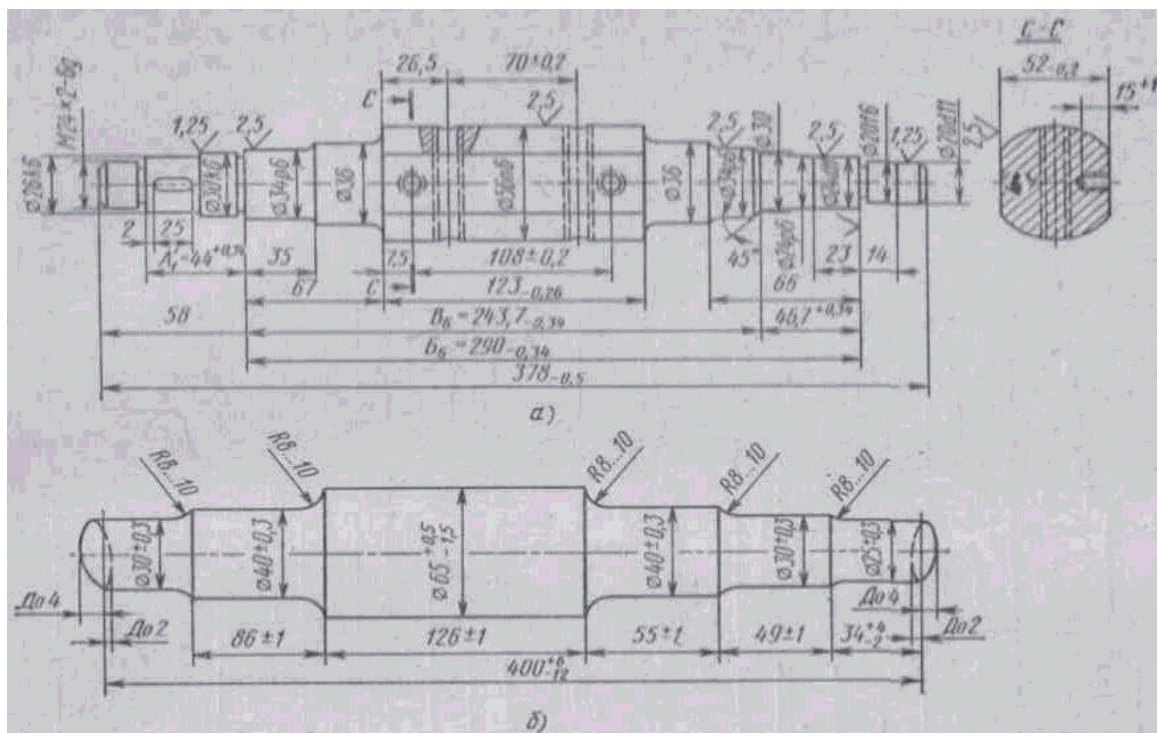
Вал генератора: а – эскиз вала; б – эскиз заготовки
